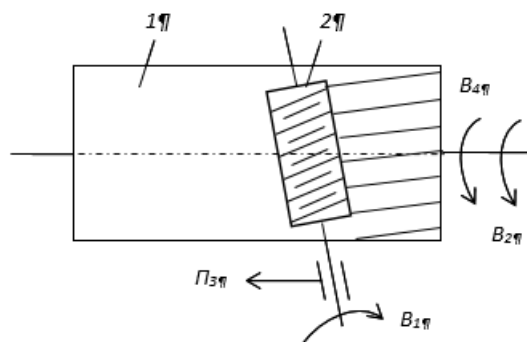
Способ фрезерования червячной фрезой шлицевых валов
